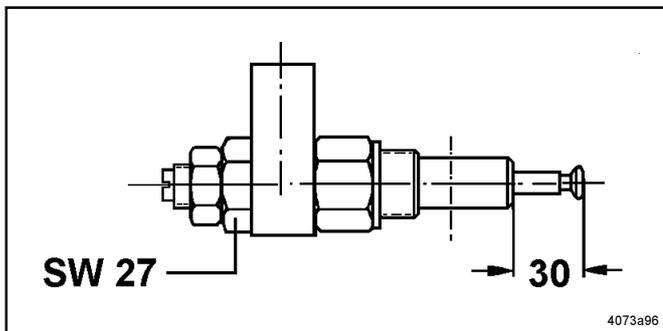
Retirer le piston pour installer l'élément de pompage
